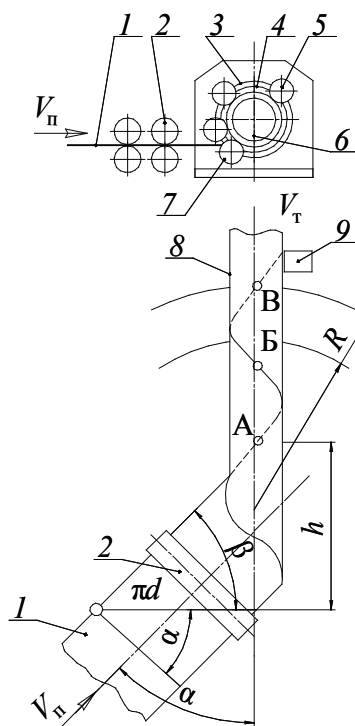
Схема формовки спиральной заготовки трубы во втулочно-роликовой машине:
